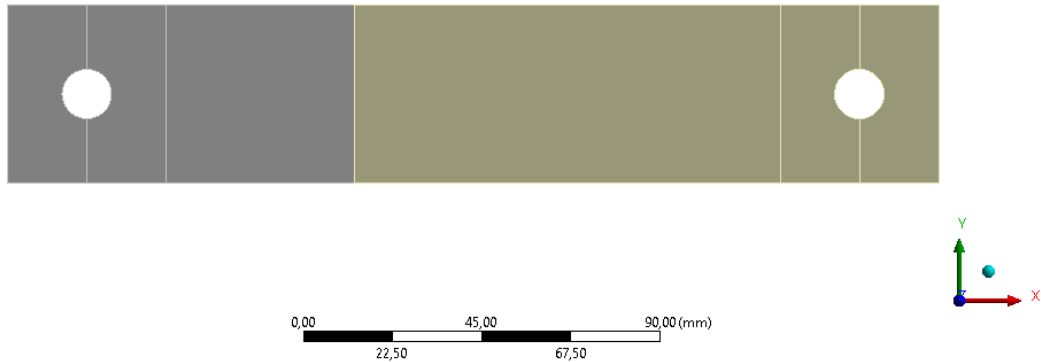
Vista frontal de la geometría de las probetas de las chapas soldadas
